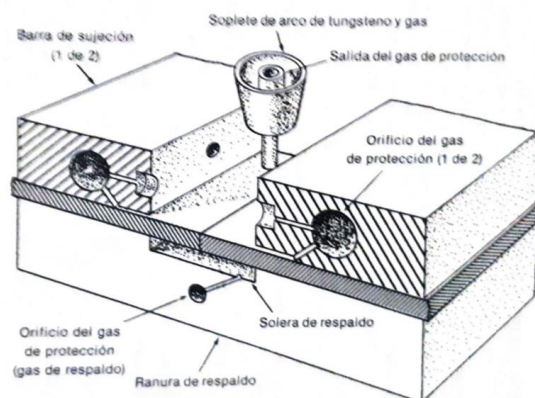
Arreglo típico en soldadura de titanio [4]
